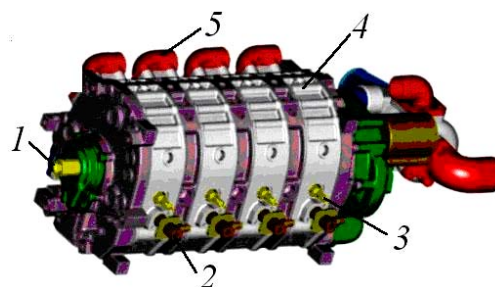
Многороторный РПД: 1 – вал двигателя; 2 – топливная форсунка; 3 – свеча зажигания; 4 – роторно-поршневая секция двигателя; 5 – выпускной коллектор
